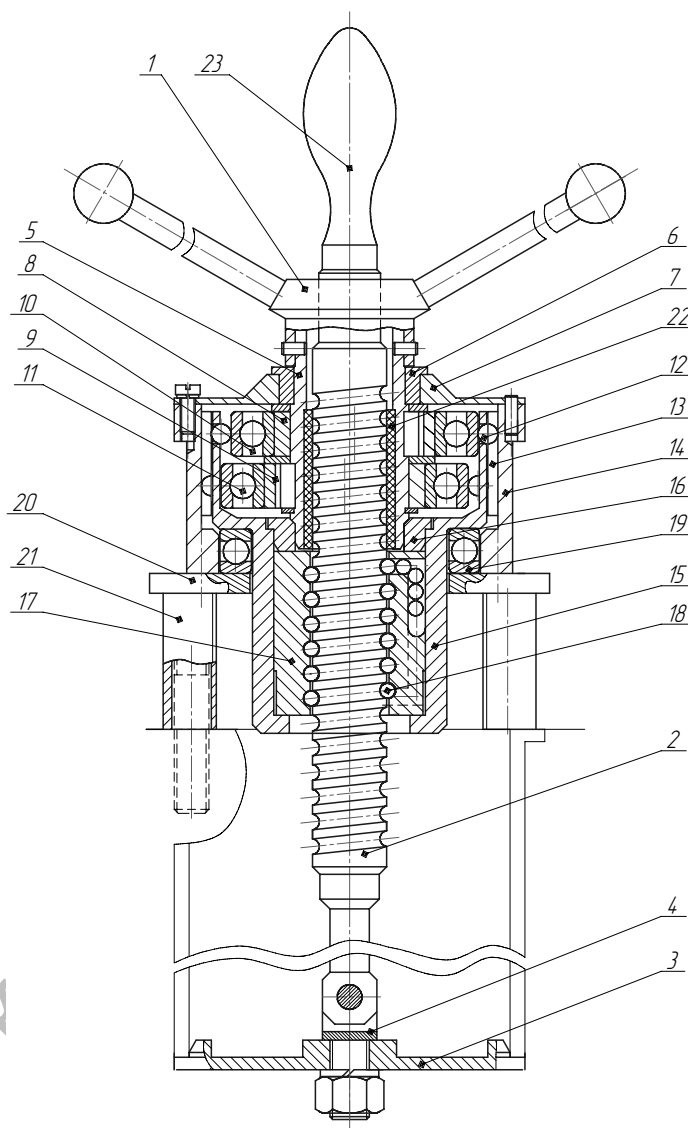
Приспособление для удаления гильз из блока цилиндров
